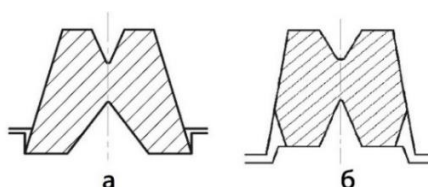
Разрезные калибры: а – полузакрытый; б – закрытый снизу
